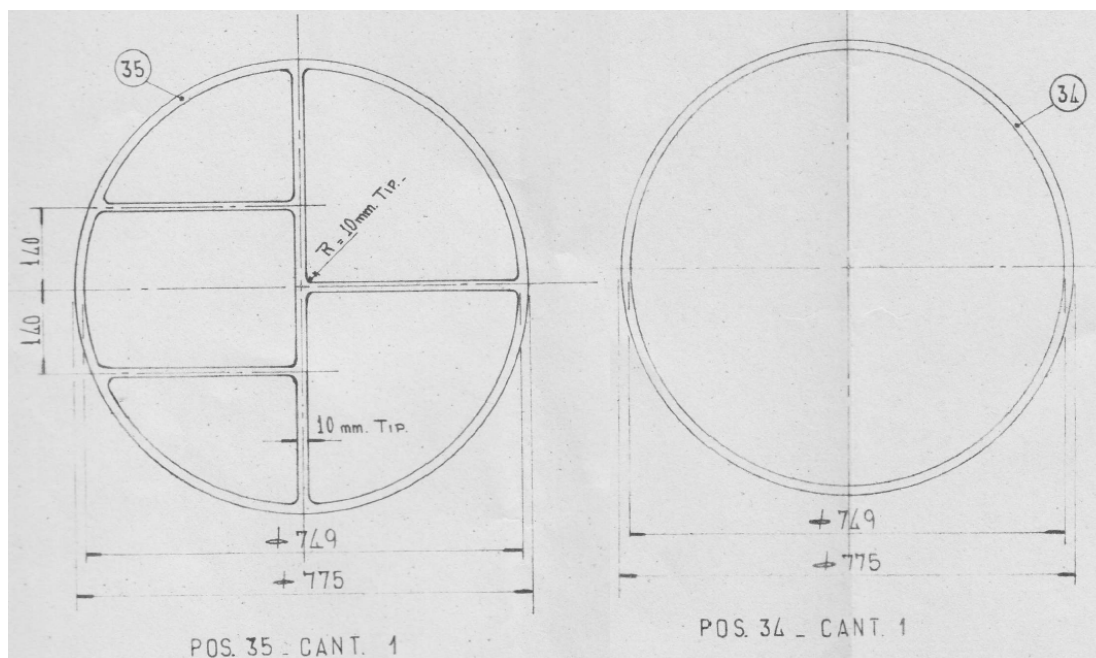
Plano de empaquetaduras enchaquetadas del 31 – 3207
